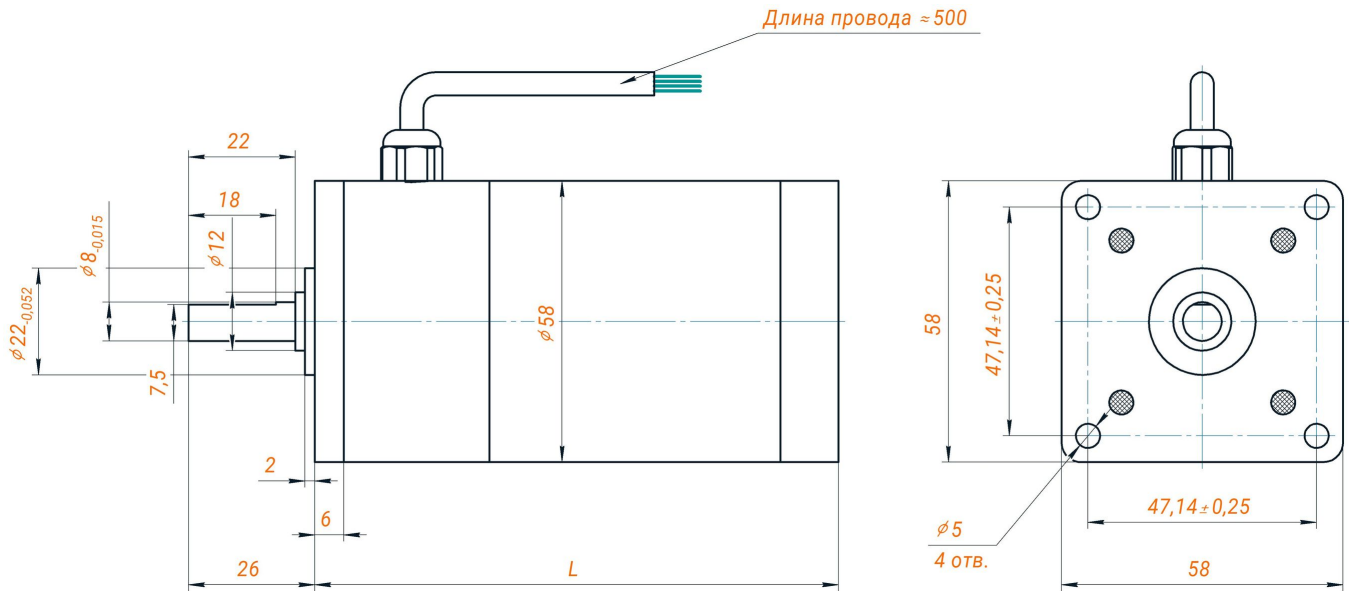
Габаритные размеры шаговых двигателей с IP68 серии 57
